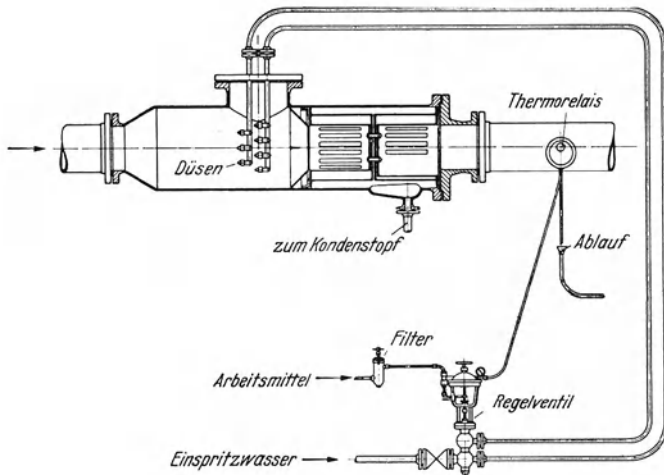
Heißdampfkühler mit Einspritzdüsen.
